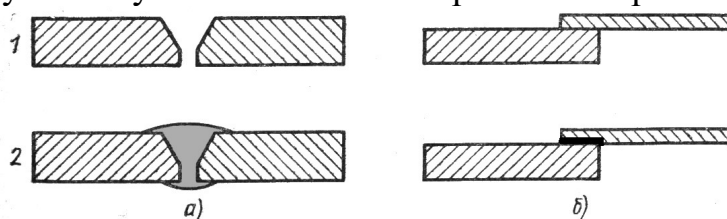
Схема пайки-сварки (а) и сварки-пайки (б)
